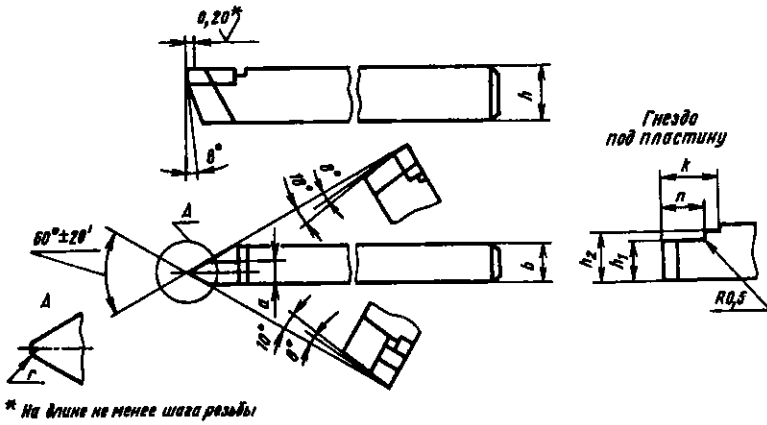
Размеры гнезда под пластину резцовых резцов для наружных резьб
